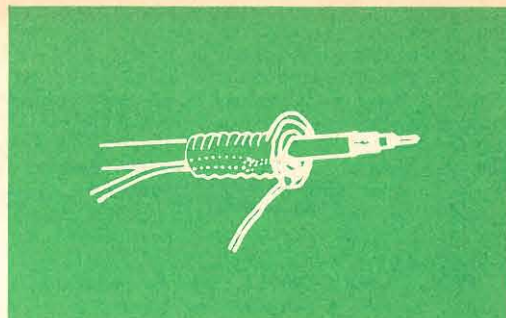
Particolare del montaggio del cavetto di massa sulla molla.
